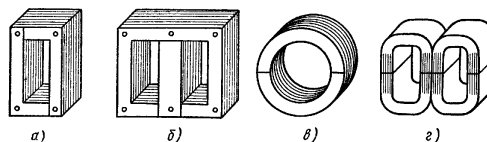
Магнитопроводы сварочных трансформаторов: а — шихтованный Г-образный; б — шихтованный Ш-образный; в — шихтованный кольцевой; г — витой Ш-образный
